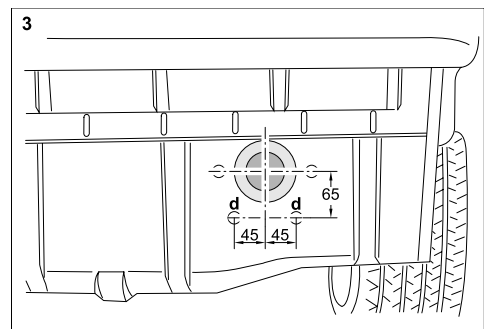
Bohrungen Heckblech rechts und Dichtring
